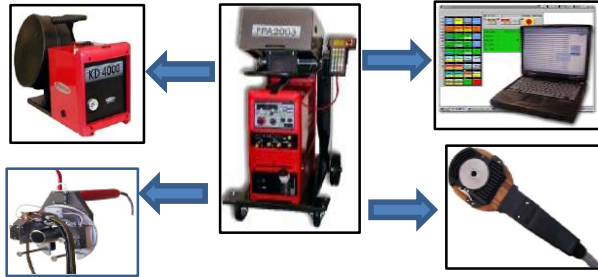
Composición de la Soldadura Orbital [4].
